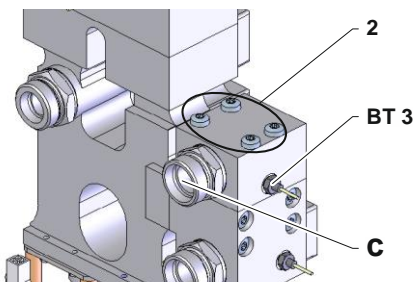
Retirer le couvercle du module de l'accumulateur
